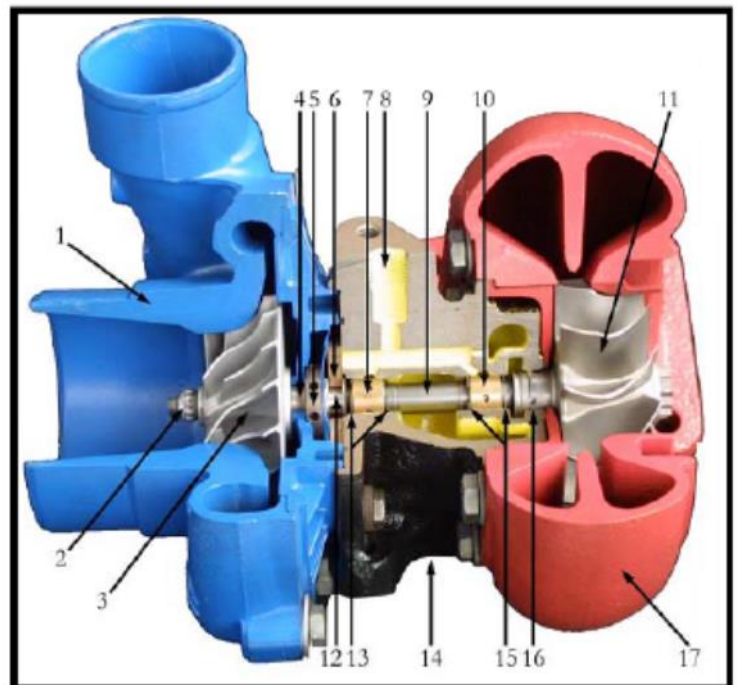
Vue en coupe d'un turbocompresseur.
